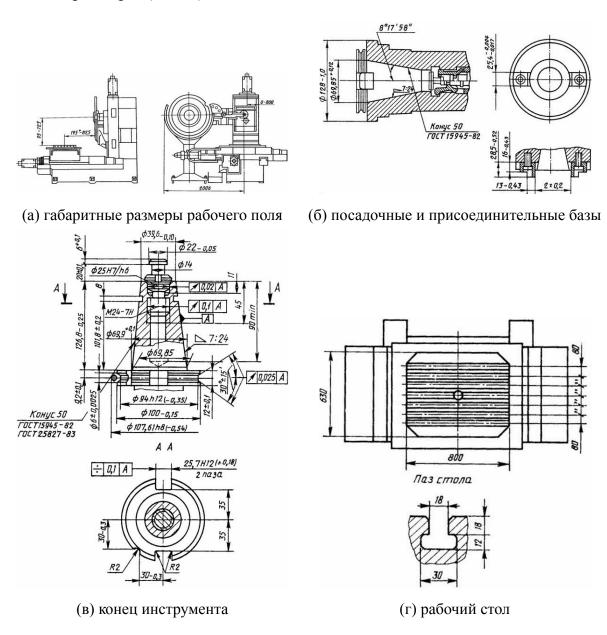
Посадочные и присоединительные размеры станка 2206ВМФ4
